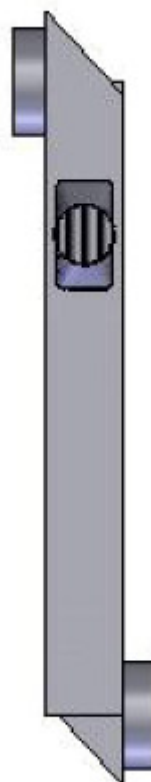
Stávající řešení geometrie tepelného výměníku
